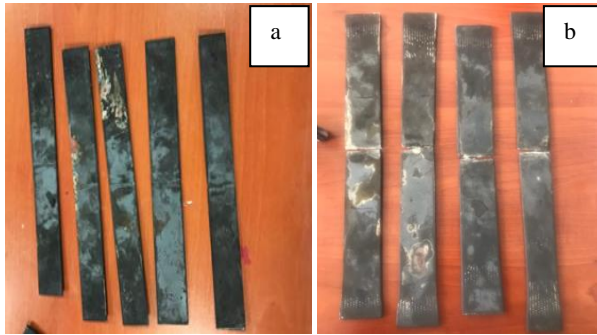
TIG kaynağı ile birleştirilmiş AISI 304 paslanmaz çelik sac numune (AISI 304 stainless steel sheet sample combined with TIG welding)
